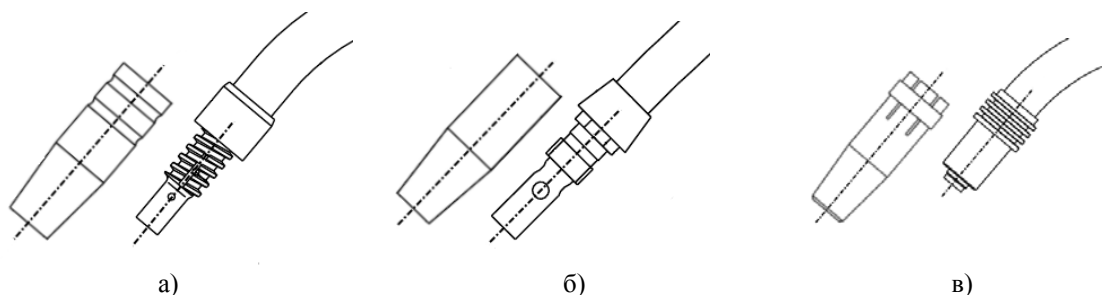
Конструкции крепления сопел к сварочным горелкам
